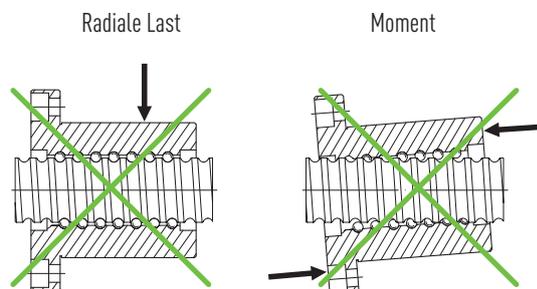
Beim Einbau des Kugelgewindetriebs dürfen keine radialen oder exzentrischen Kräfte auf die Mutter oder die Spindel wirken
